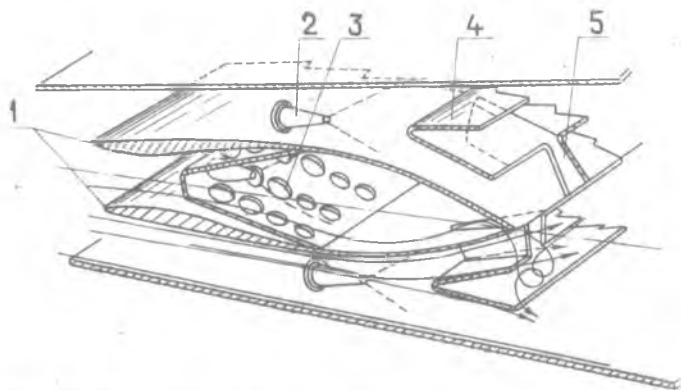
Форкамера с большим числом плоских струй; 1 — форкамера; 2 — форсунки; 3 — фронтное устройство; 4 — V-образный стабилизатор; 5 — каналы для струй пламени
